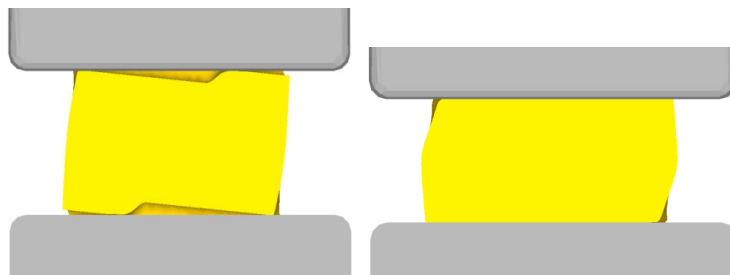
Заготовка до и после протяжки в плоских бойках
